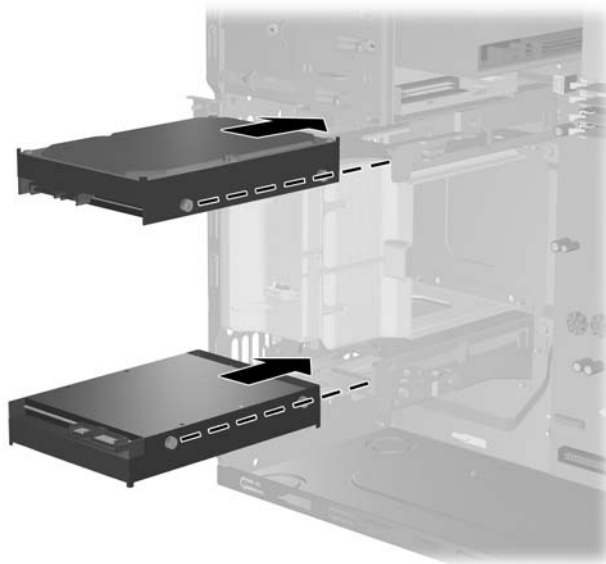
Anbringen der Festplattenführungsschrauben
